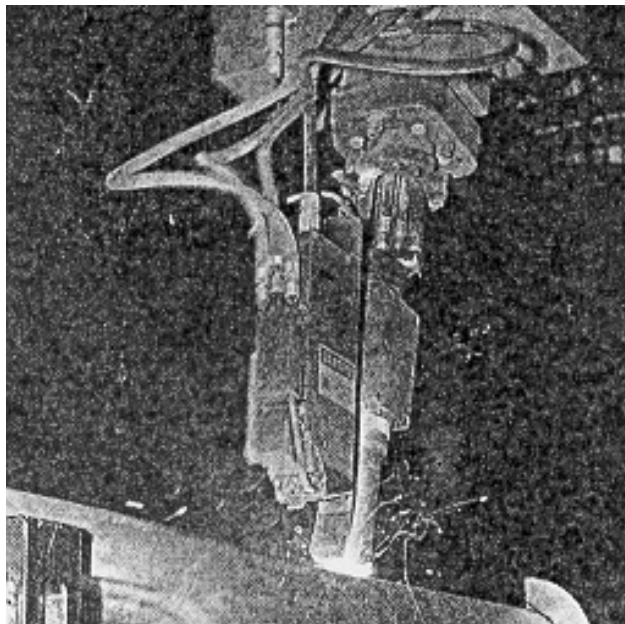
Sensor laser Seampilot adaptado a uma tocha de soldagem por arco.
